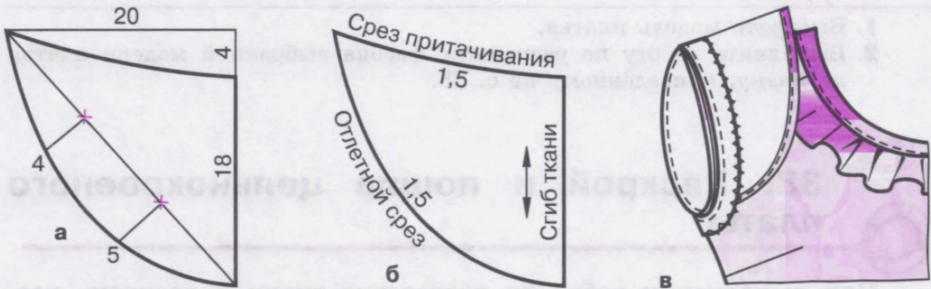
Построение чертежа оборки «крылышко» для обработки срезов пройм (а), подготовка выкройки оборки к раскрою (б) и обработка оборкой среза проймы изделия (в)
